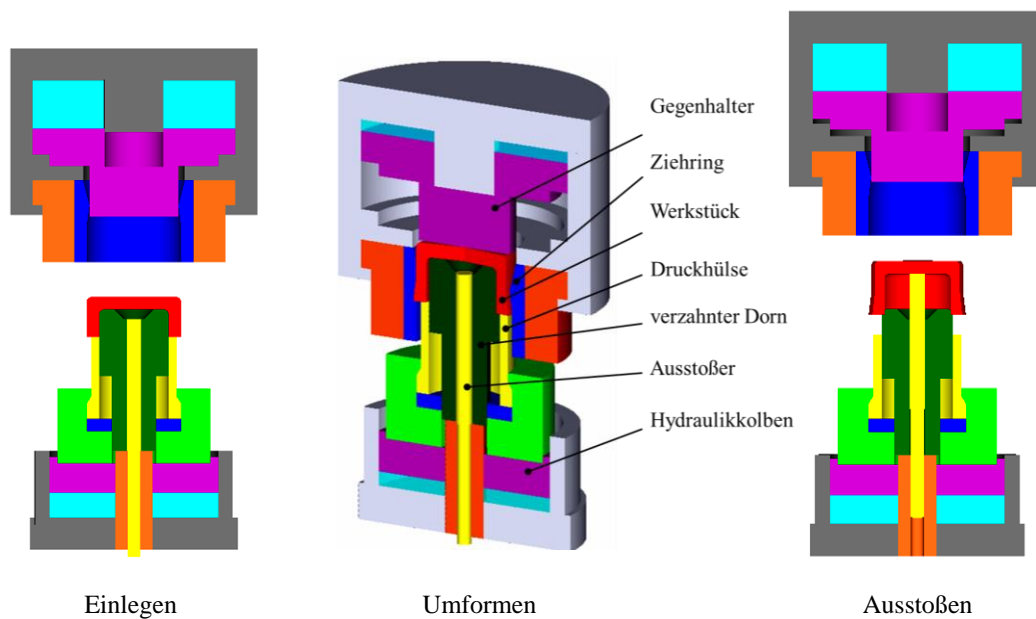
Werkzeugprinzip und Prozessablauf der Herstellung von schrägverzahnten Hohlrädern [Sch03]
